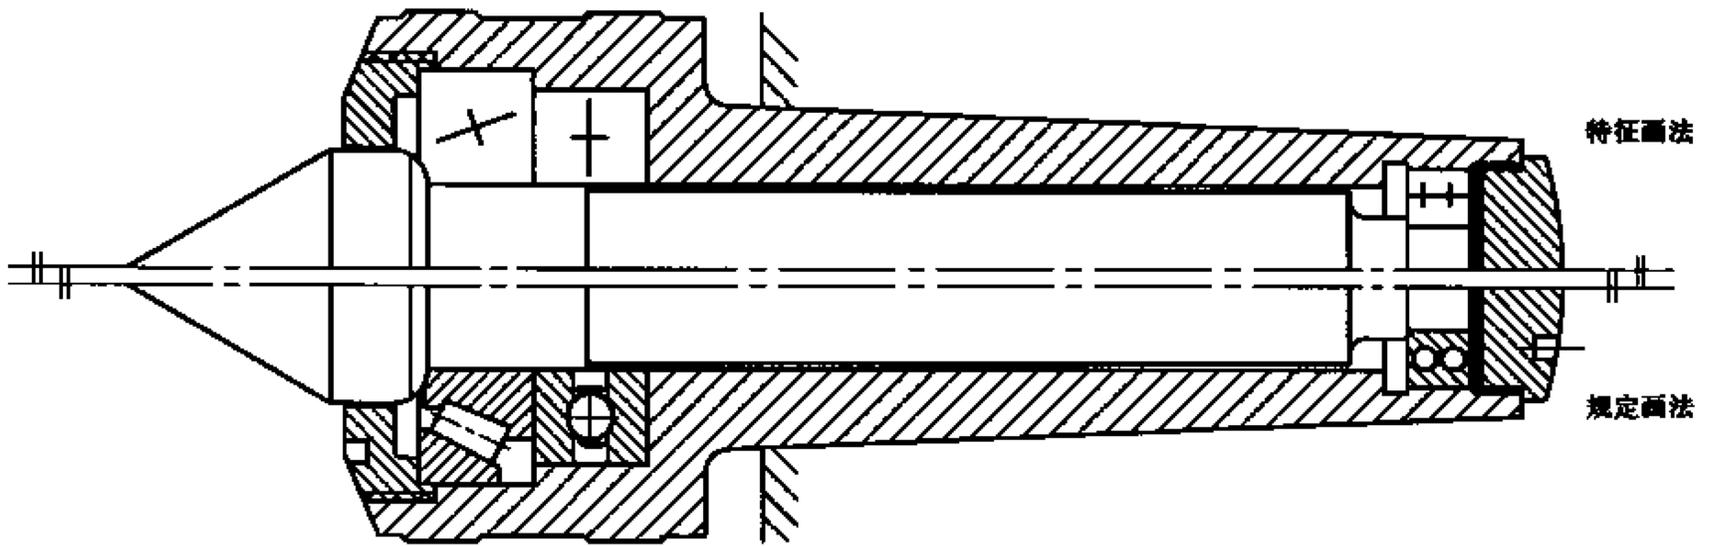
圆锥滚子轴承、推力球轴承和双列深沟球轴承在装配图中的画法
